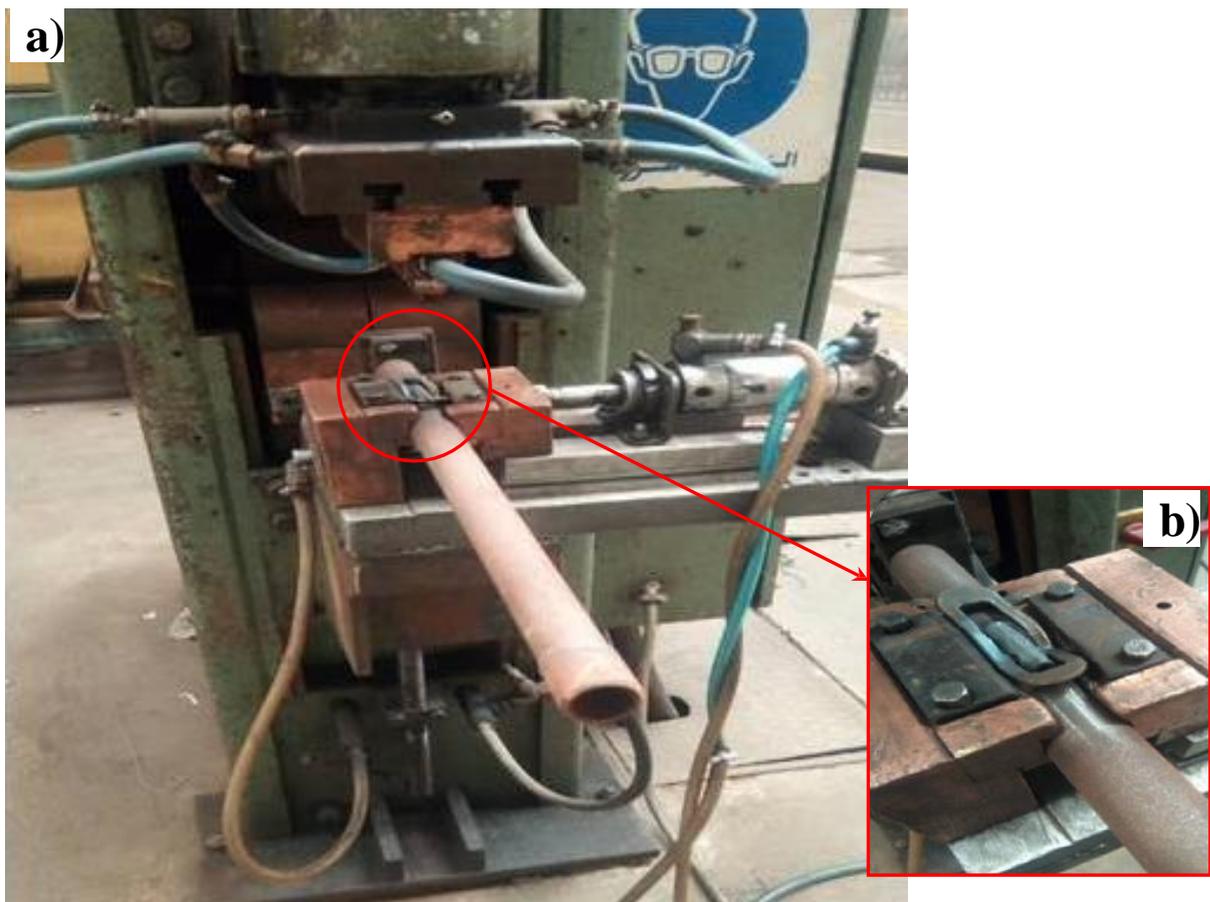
Machine de soudage par point (DALEX) ; a) Vision générale ; b) Fixation de rallonge [3]
